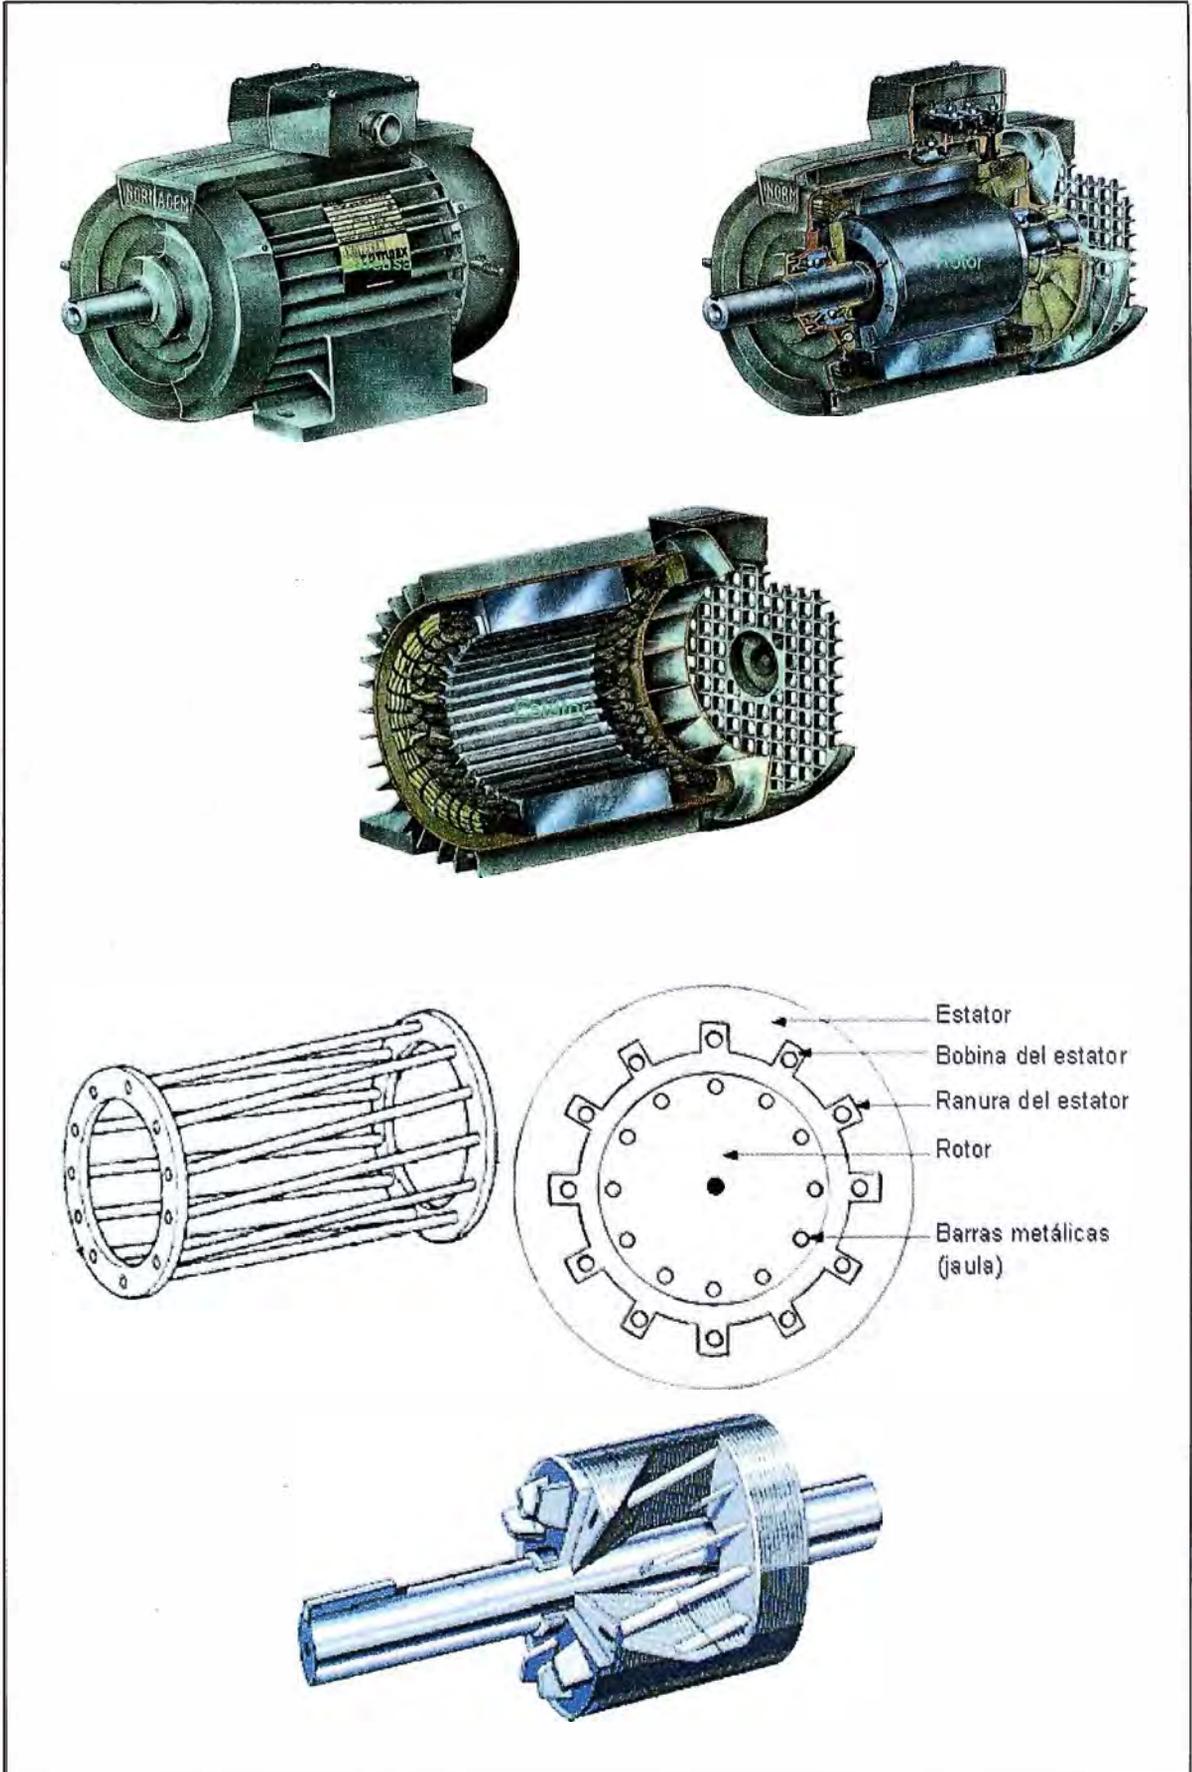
Partes del Motor con rotor de jaula de ardilla
